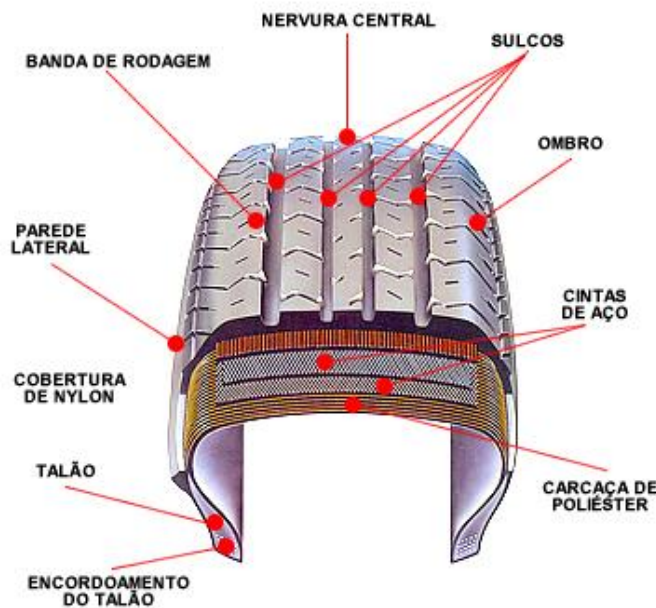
Partes componentes da estrutura de carcaça de um pneu de passeio
